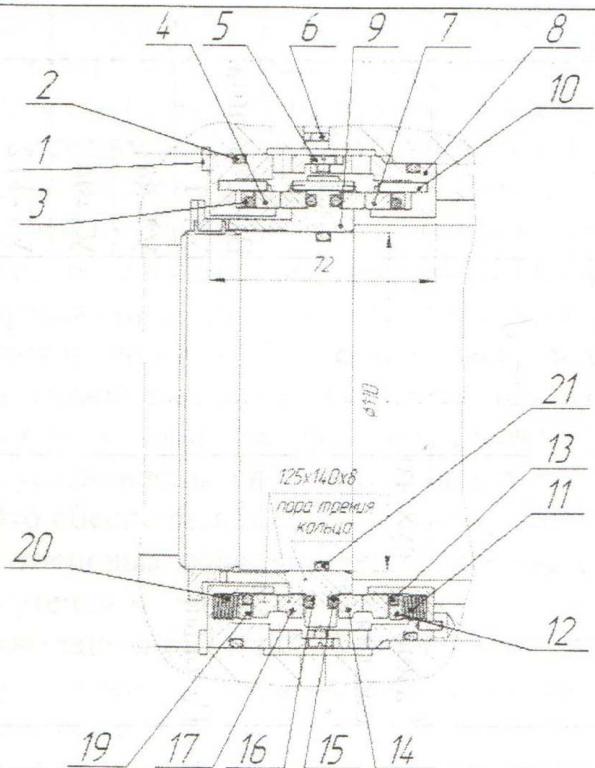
Двухстороннее торцевое уплотнение пакетного типа: 1 - кольцо стопорное; 2,3,13,15,16,21 - кольцо уплотнительное; 4,7,14,17 - кольцо графитовое; 5 - винт; 6 - жиклер; 8 - корпус; 9 - втулка; 10 - штифт; 11,20 - пружина; 12,19 - кольцо
